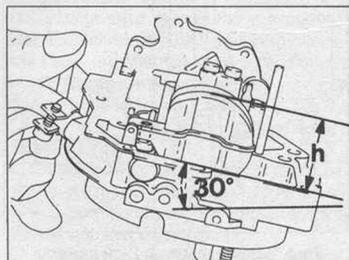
Контрольные размеры положения поплавка (Глава 16)
